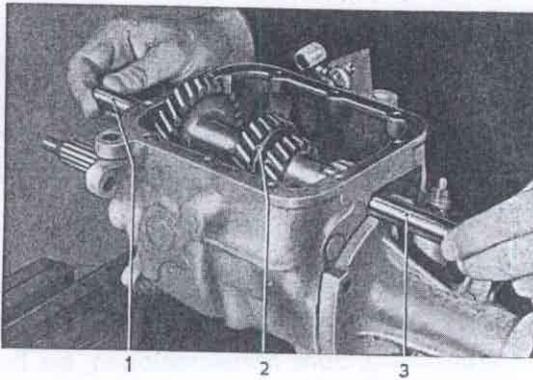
Achse für Nebenwellen-Zahnradblock ausführen
